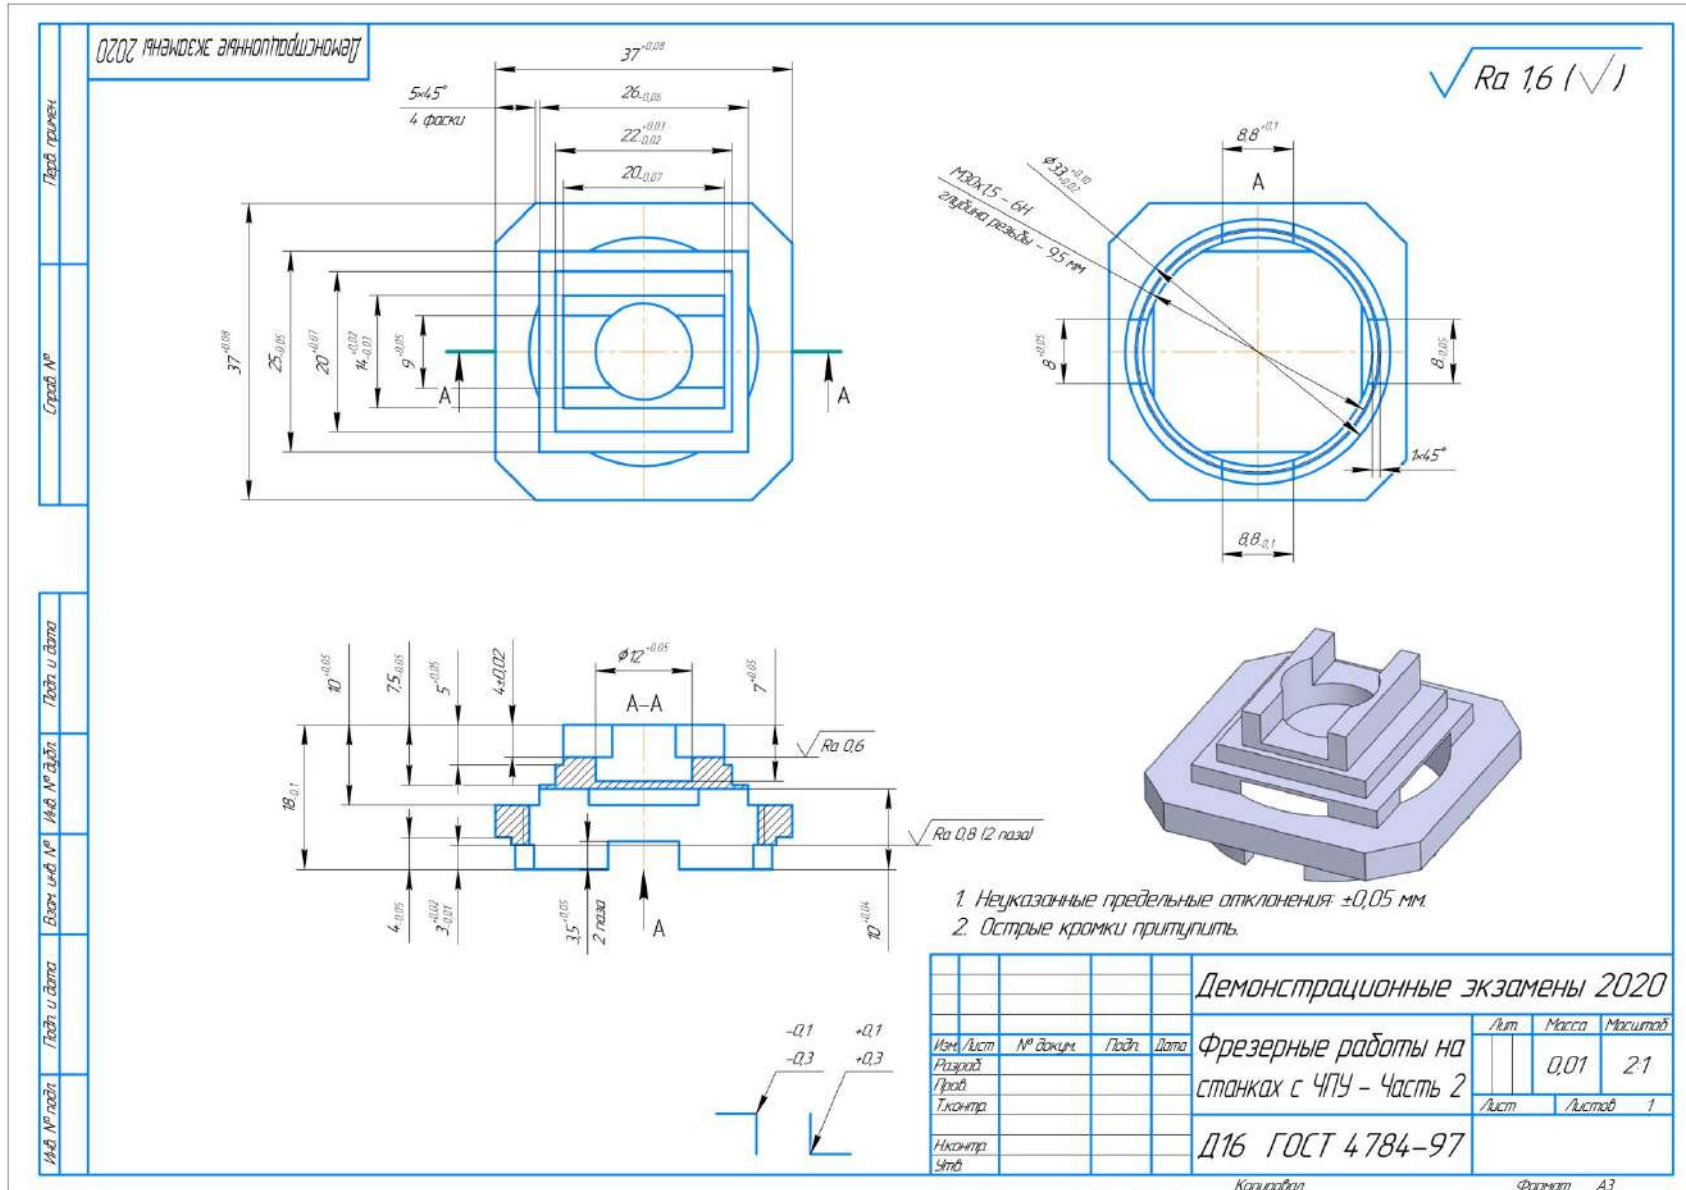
Чертеж детали Фрезерные работы на станках с ЧПУ
